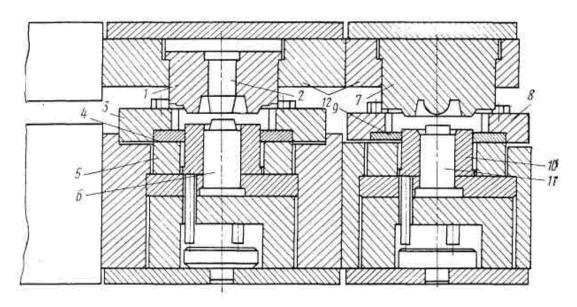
Схема формообразующих вставок штампа кривошипного горячештамповочного пресса для штамповки поковки шестерни: чистовой ручей (в центре): 1 – пуансон; 2 – верхний прошивень; 3 – зубчатый вкладыш; 4 – опорное кольцо-вставка; 5 –вкладыш-выталкиватель; 6 – нижний прошивень; черновой ручей (справа): 7 – пуансон; 8 – зубчатый вкладыш; 9 – опорное кольцо-вставка; 10 – вкладыш-выталкиватель; 11 – прошивень; 12 – призматические универсальные вставки для крепления формообразующих вставок
